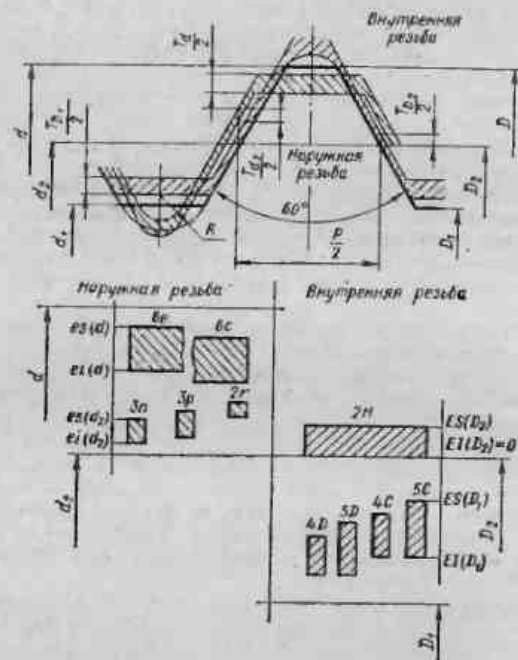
Расположение полей допусков резьбы с натягом;
